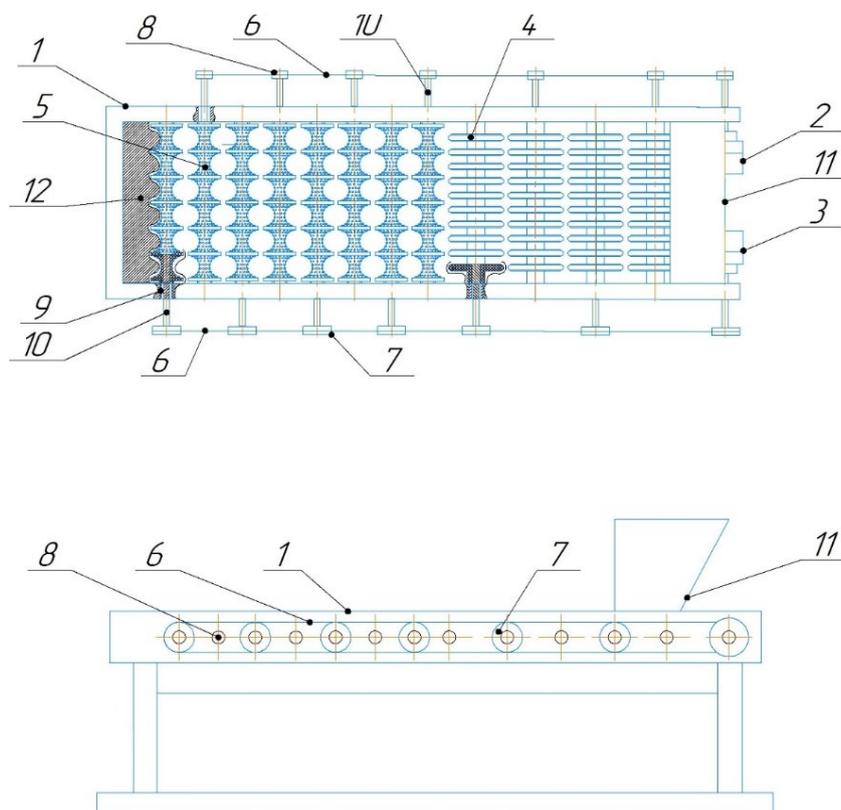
Установка для очистки корнеплодов от почвы [8]: 1 – рама; 2 и 3 – приводы; 4 и 5 – вальцы; 6 – цепь; 7 и 8 – звездочки; 9 – втулки; 10 – валы; 11 – бункер; 12 – скатная доска
